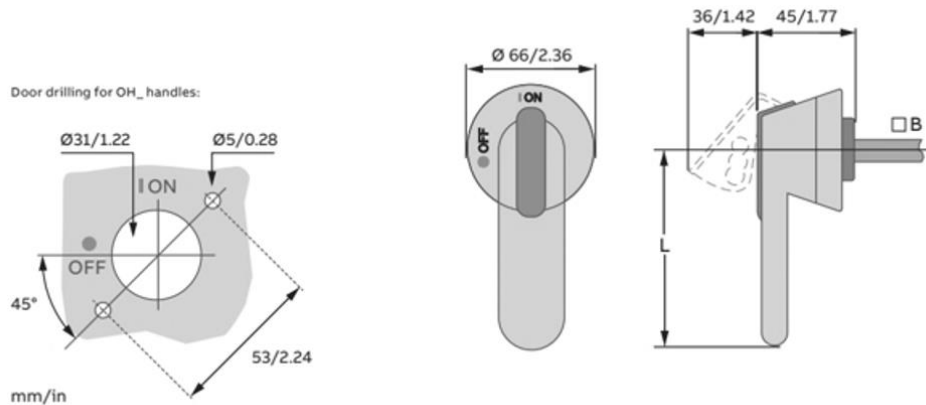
Griff-Montageanleitung Darin sind die Montageanleitung für den Griff und die geometrischen Details des Pistolengriffs abgebildet.
